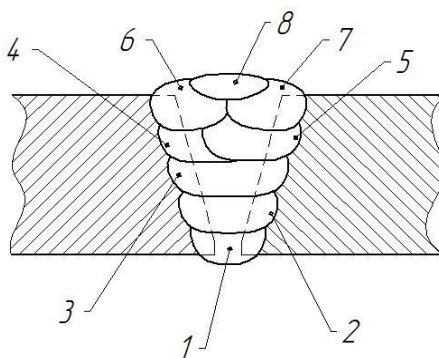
Сварное соединение и порядок наложения валиков в вертикальном стыке
